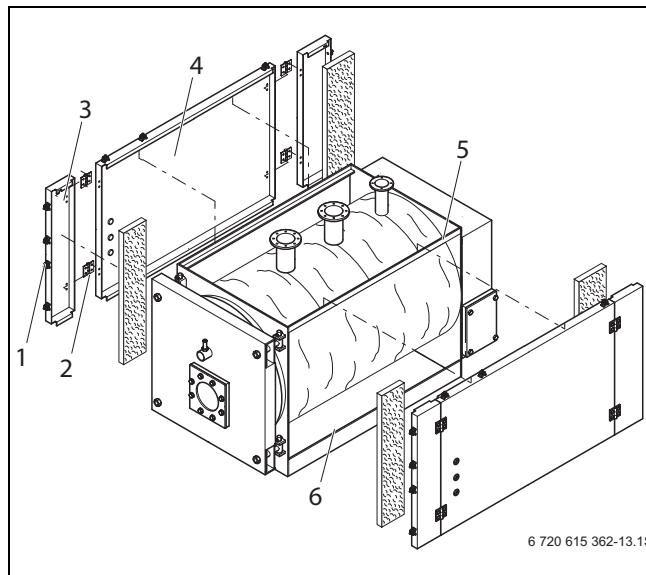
Монтаж боковых стенок в котлах 120 - 420 кВт
